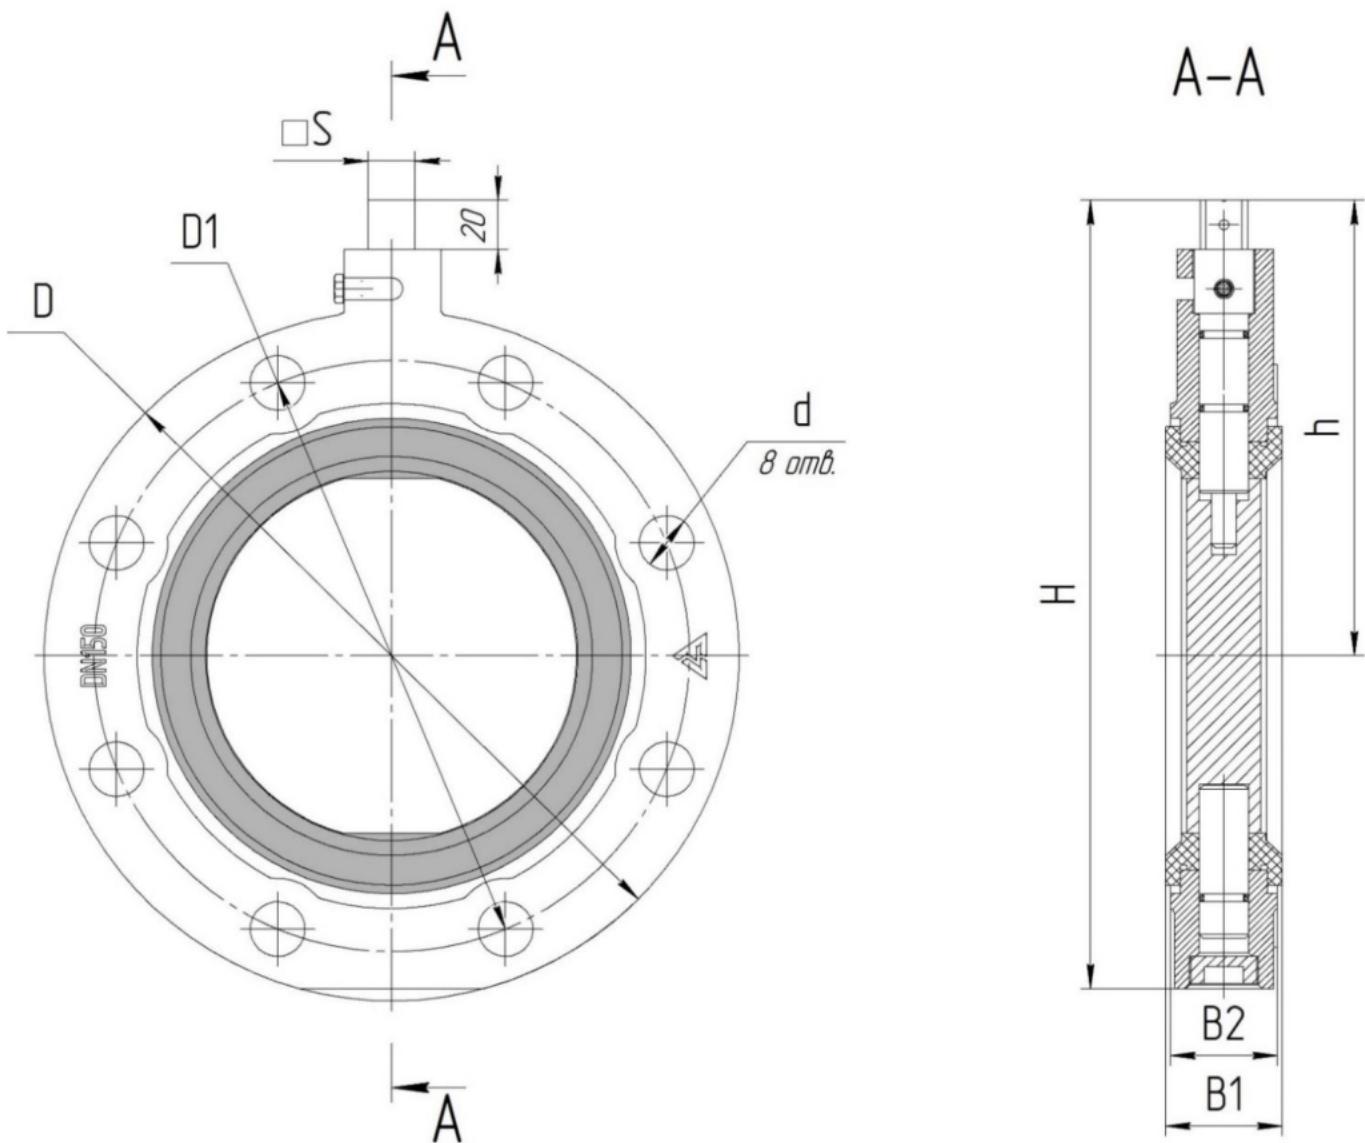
Установочные, габаритные, присоединительные размеры ЗПД
